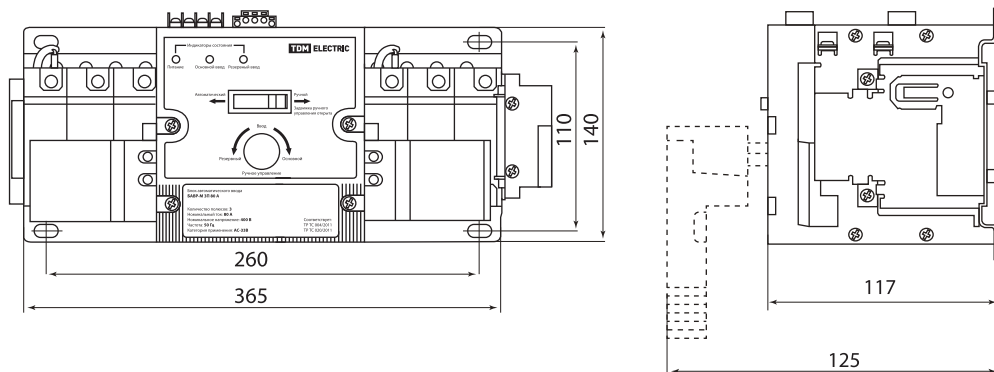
Габаритные и установочные размеры BABP-M 3П 80, 100 А, 125 А, мм
